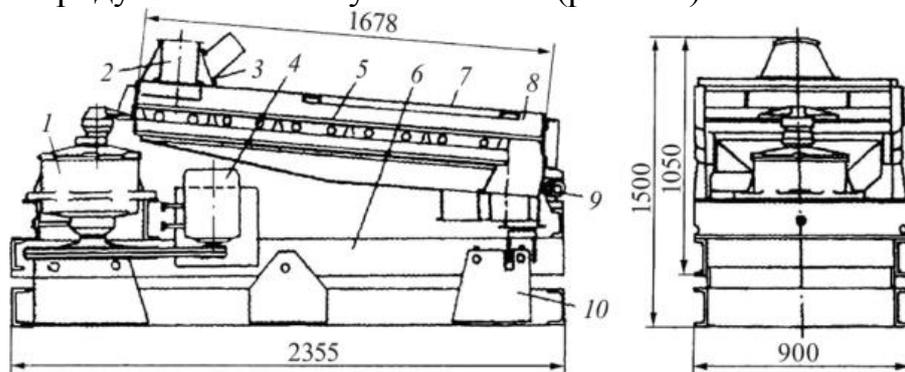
Конструкция просеивателя А1-КСБ: 1 - эксцентриковый колебатель; 2 - приемный бункер; 3,7 - крышки; 4 - электропривод; 5 - ситовый корпус; 6 - рама; 8 - сменные рамки; 9 - тяга; 10 - станина
